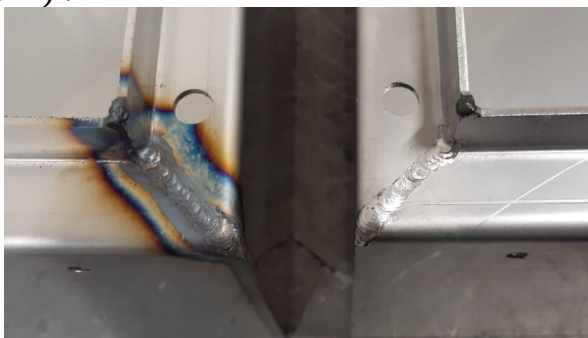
Пассивация сварных швов нержавеющей стали
